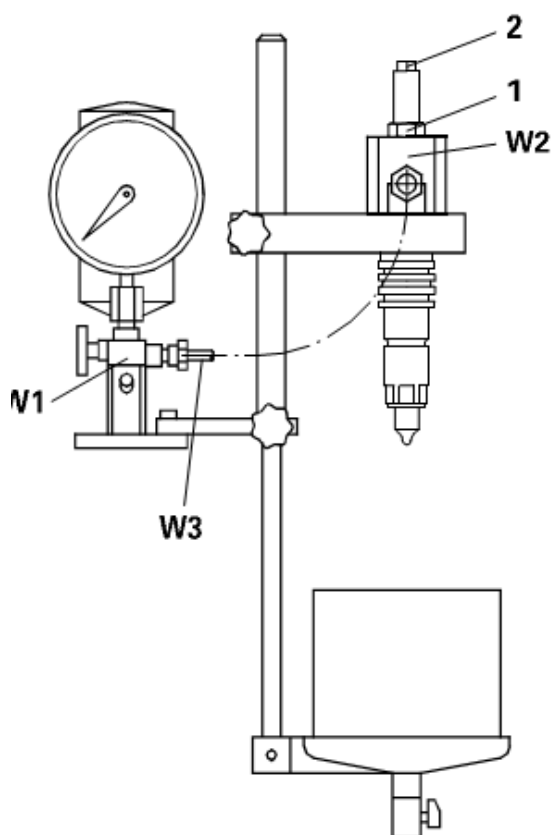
Контрольний пристрій паливних форсунок
